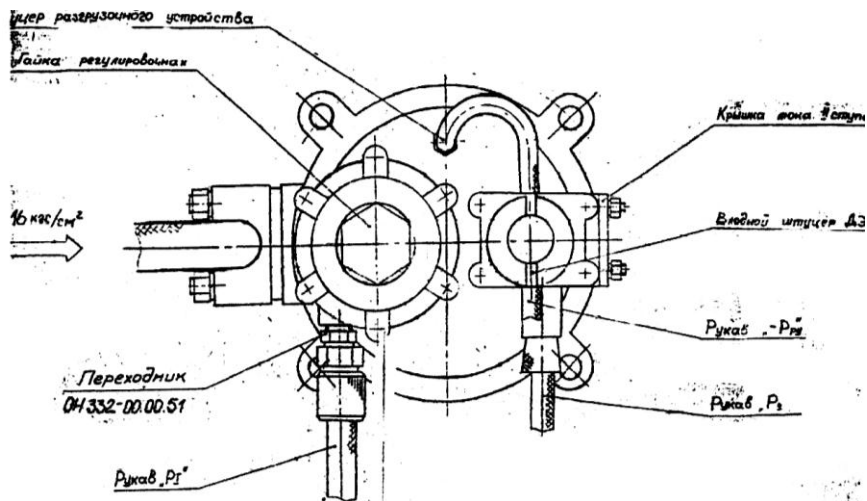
Схема для проверки на герметичность разгрузочного и экономайзерного устройств
